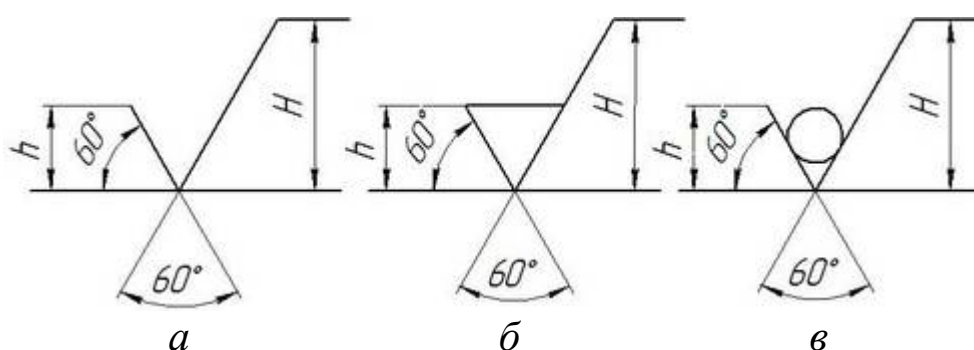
Условные знаки для обозначения шероховатости поверхности
